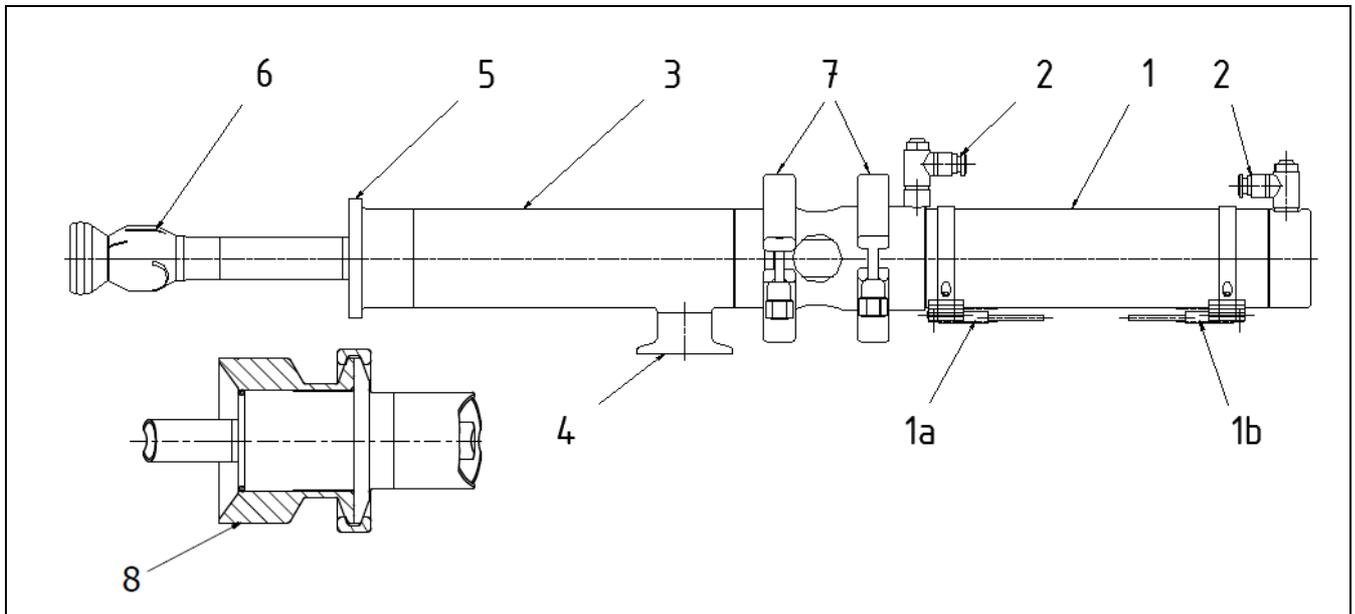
Prinzipieller Aufbau des Gerätes
